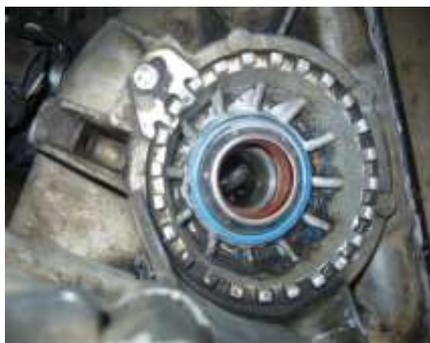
Montaje de Retenedor Semieje Lado Izquierdo
